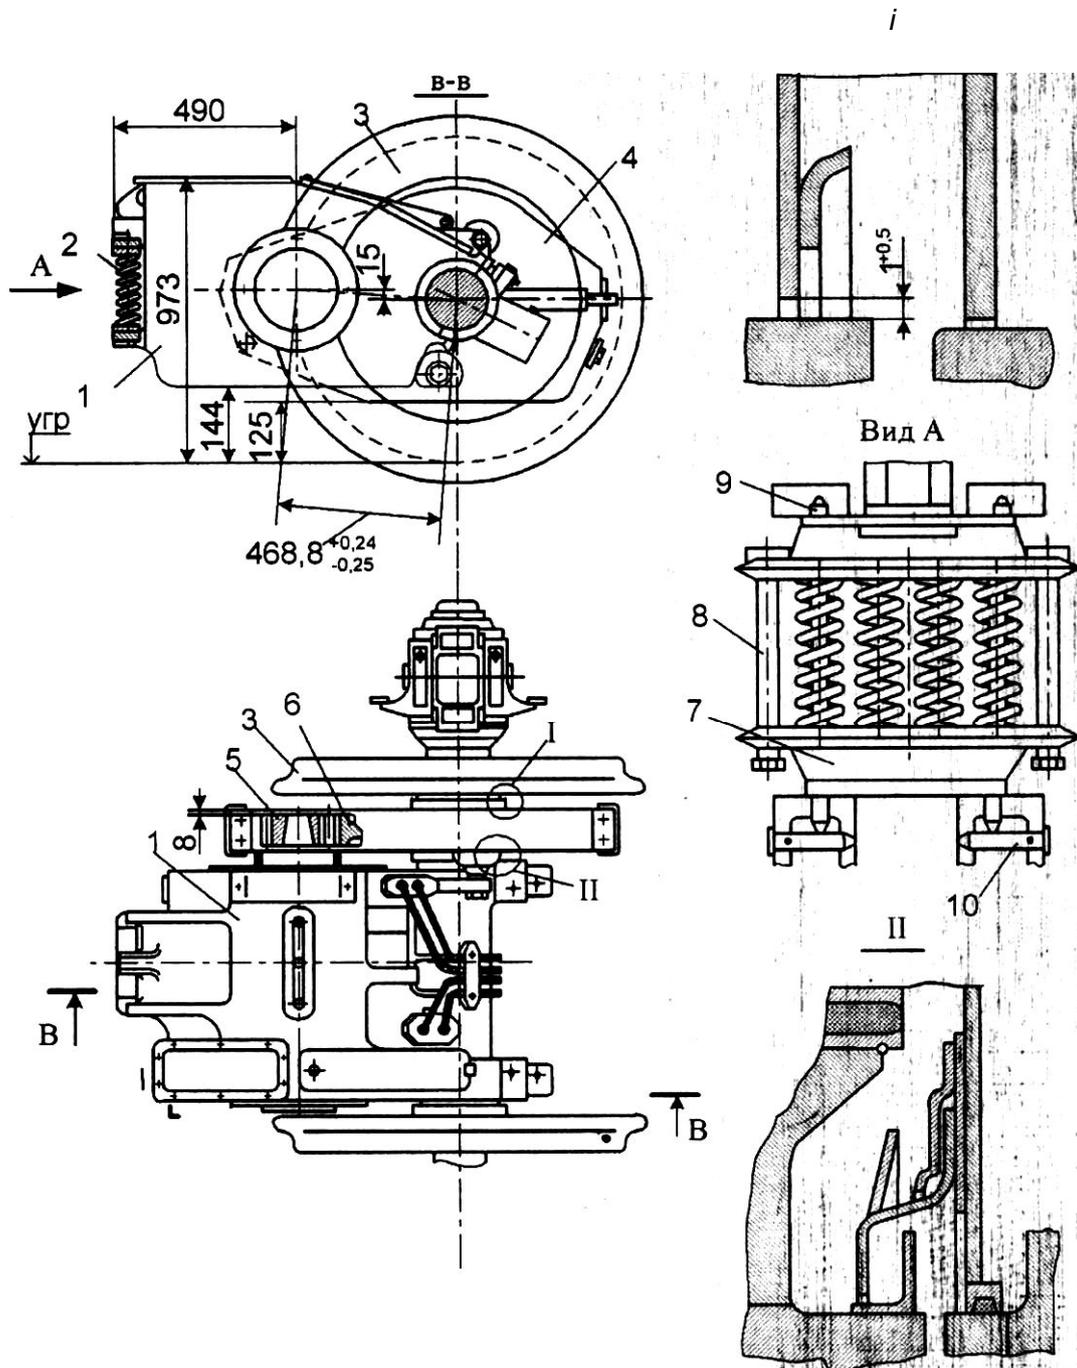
Колесно-моторный блок (привод I класса): 1-ТЭД; 2-пружинный комплект; 3-колесо; 4-кожух; 5-ведущая шестерня; 6-зубчатое колесо; 7-балки-опоры пружинного комплекта; 8-стягивающие болты; 9-фиксирующие стержни; 10-поперечные валики
